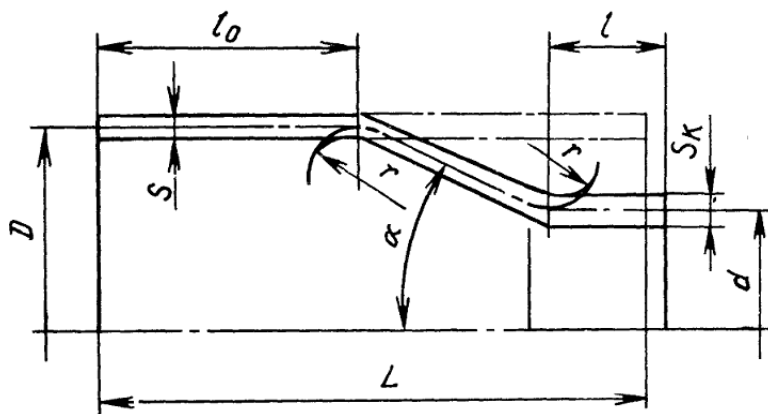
Схема к определению размеров заготовки при обжиге (б)
